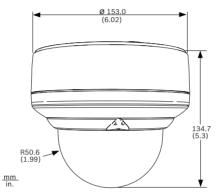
Dimensões do suporte para montagem saliente para interior
